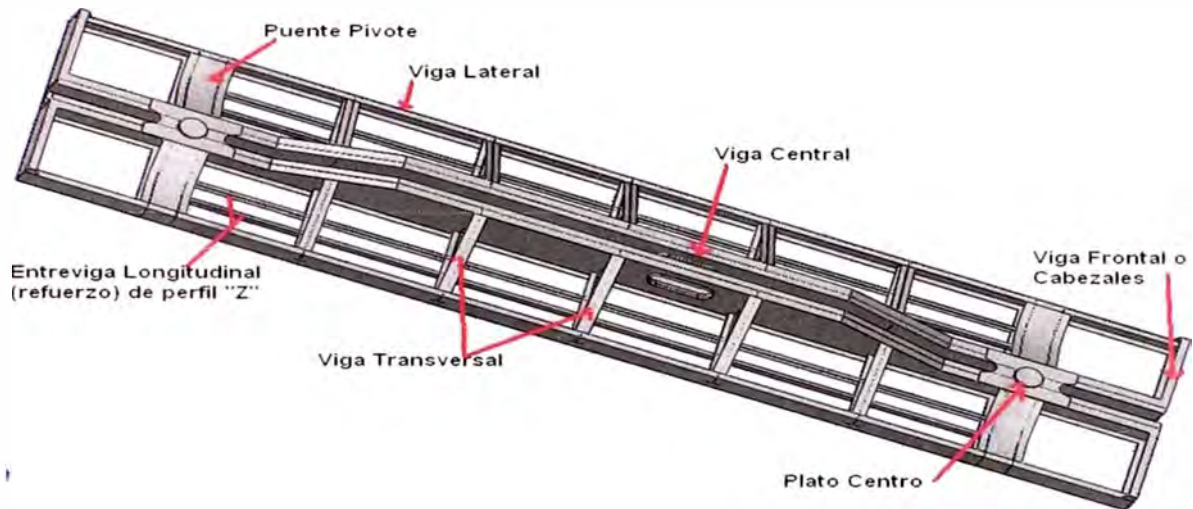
Nomenclatura de la estructura principal de un carro ferroviario
